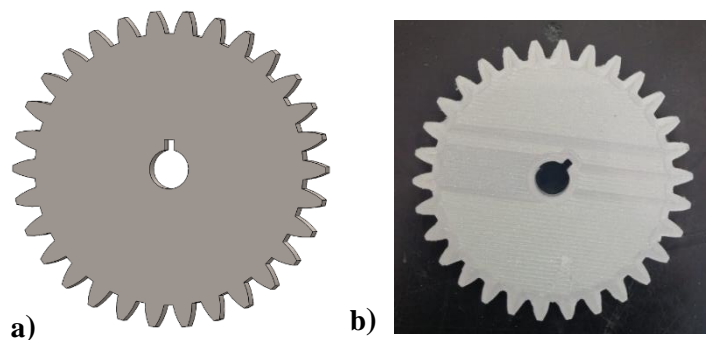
a) Desenho 3D engrenagem 30 dentes b) Impressão da engrenagem 30 dentes
